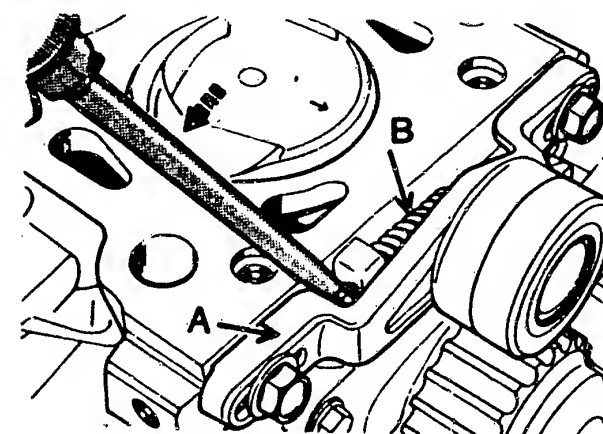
CVH-Motor: Der Zahnriemenspanner (A) mit der Feder (B) ist vor dem Festschrauben mit einem Schraubenzieher so weit wie möglich nach links zu drücken, um später den Zahnriemen leicht auflegen zu können.
